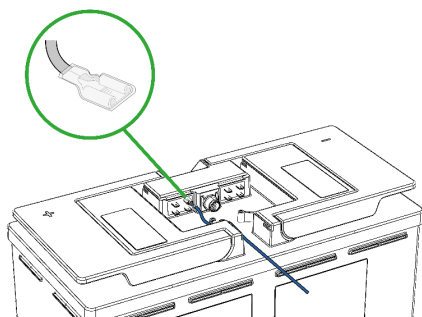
Collegamento dell'interfaccia LIN tramite connessione FASTON
